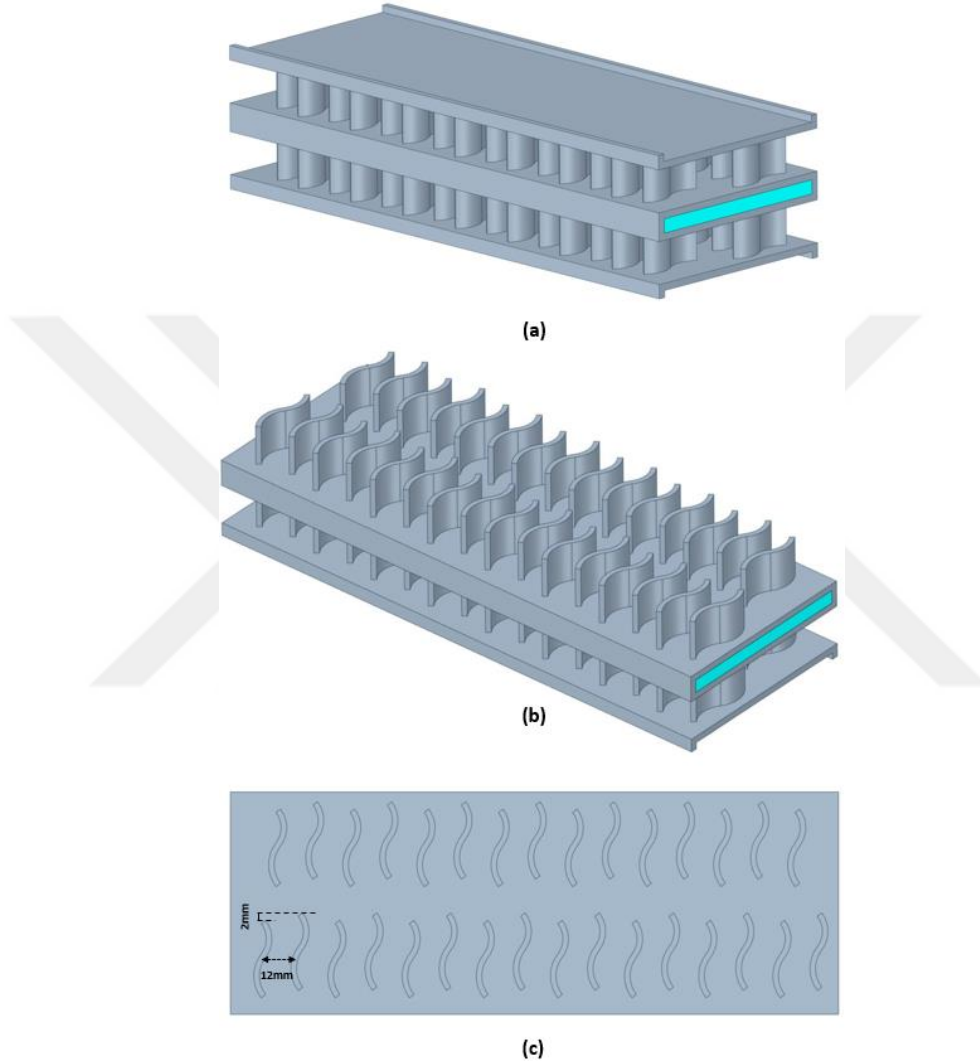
Alternatif hava kanatçığı profil kesitleri
